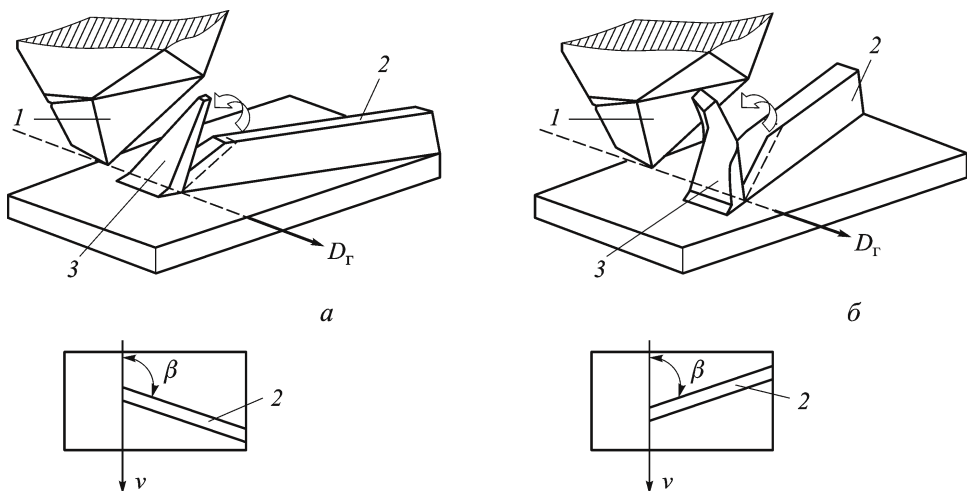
Схема формирования шипов-иглолок (а), винтовых шипов и шипов-крючков (б):
